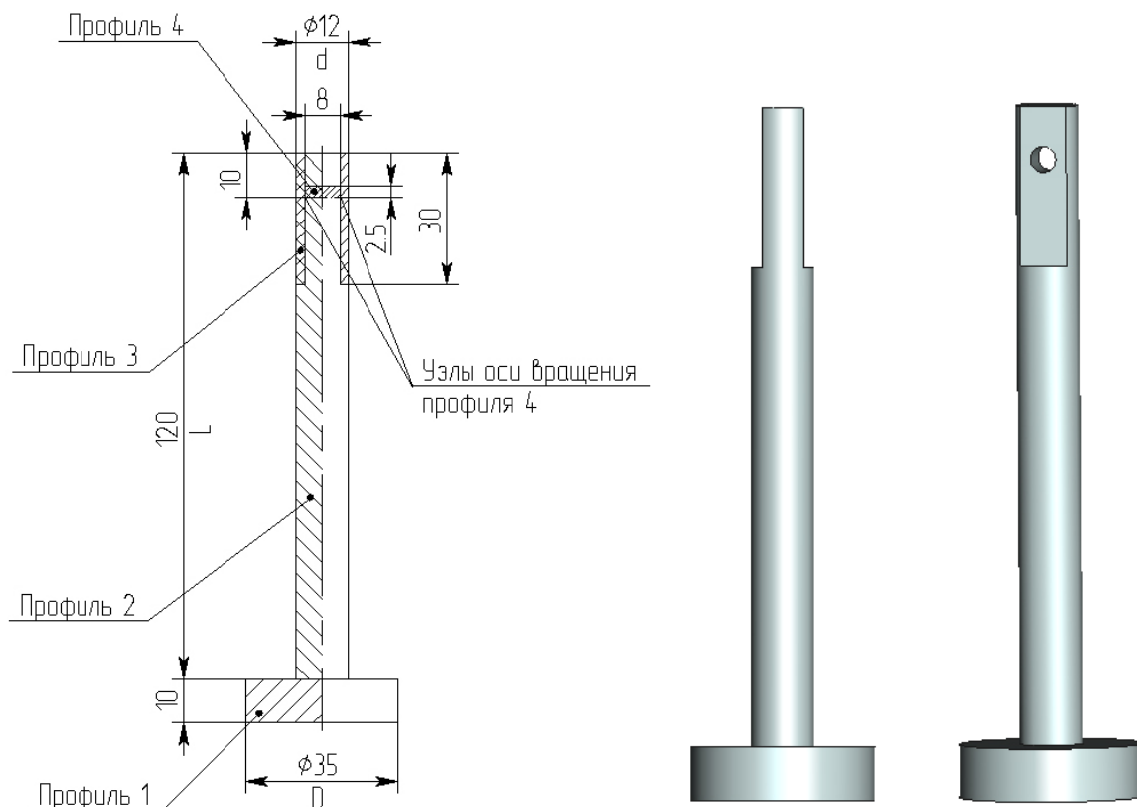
Чертеж и 3Dмодель детали «Поршень»
